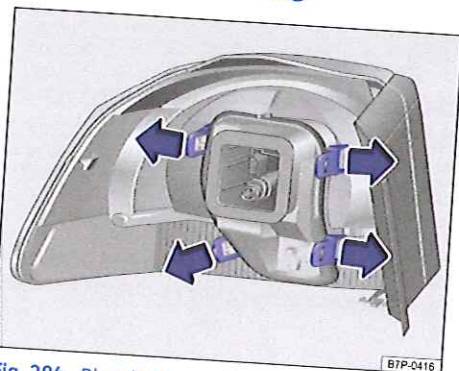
Bloc de feux arrière dans la carrosserie : épose du porte-ampoule.
